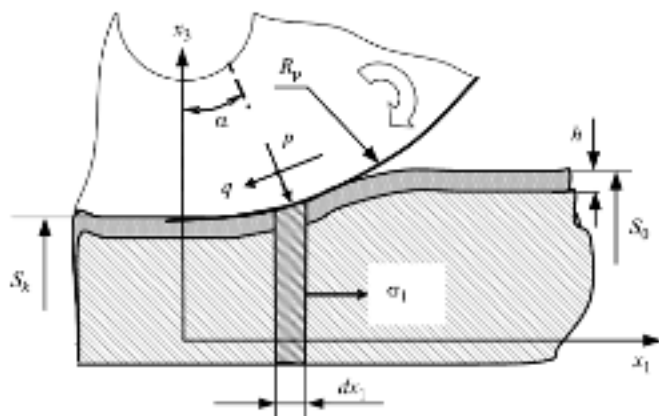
Схема локального обжима и параметры заготовки и инструмента
